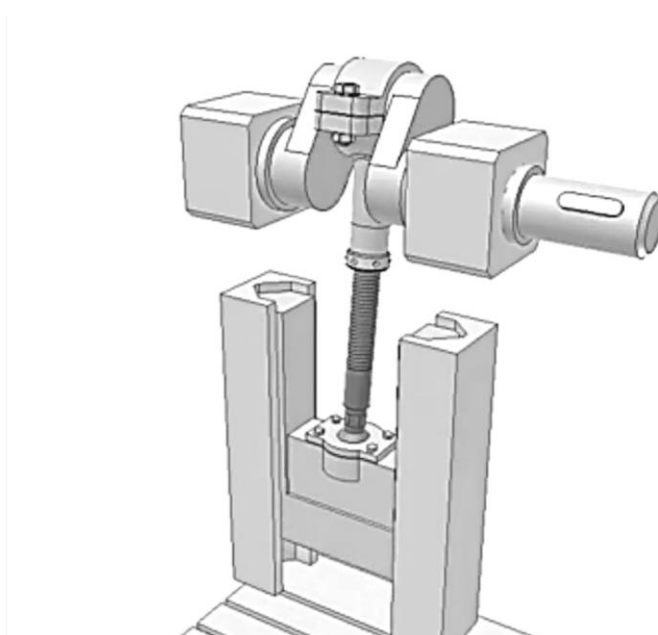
Главный исполнительный механизм кривошипного прессы
